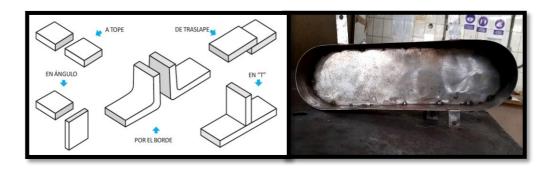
Preparación de Juntas para Soldadura (Soldexa, 2012, p. 53).
